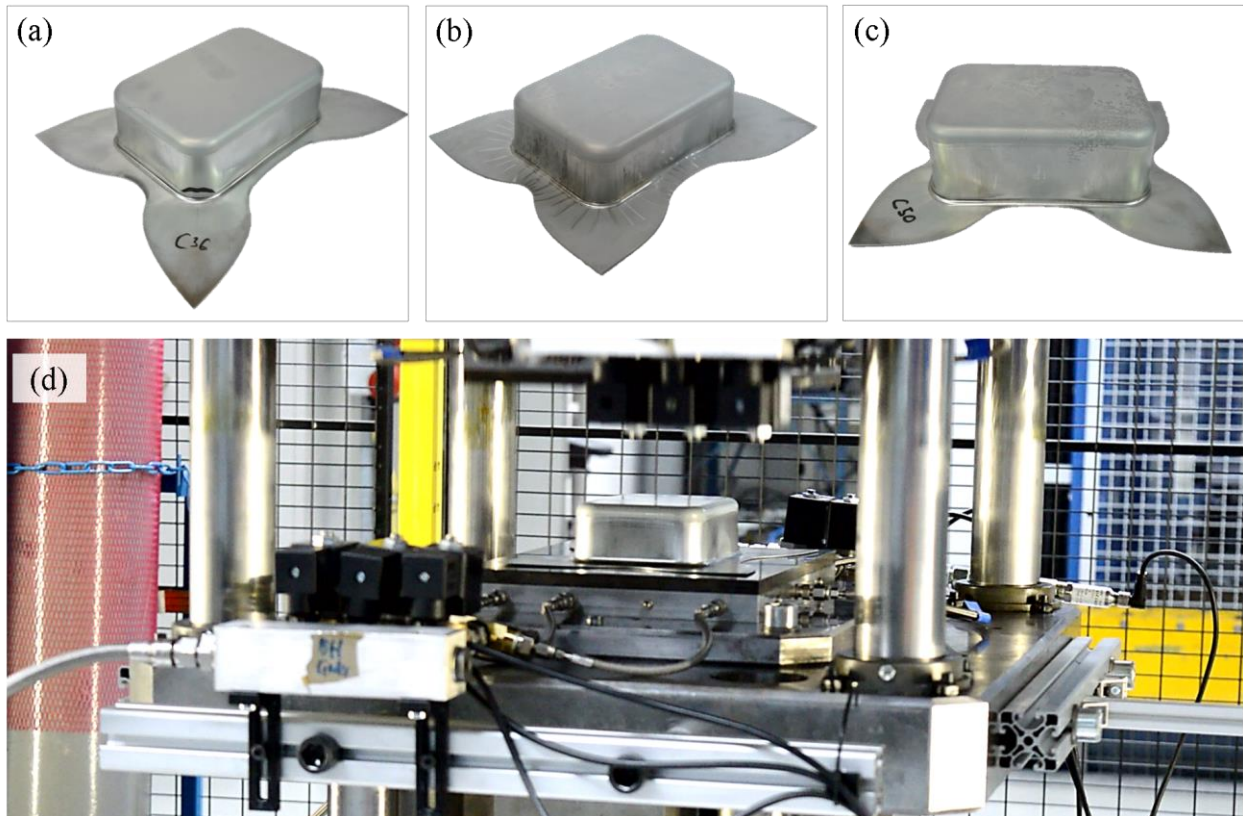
Rechtecknapf mit (a) Reißen, (b) Faltenbildung im Flanschbereich und (c) ohne Bauteilfehler tiefgezogen mit einem (d) Tiefziehwerkzeug mit aerostatischer Schmierung.
